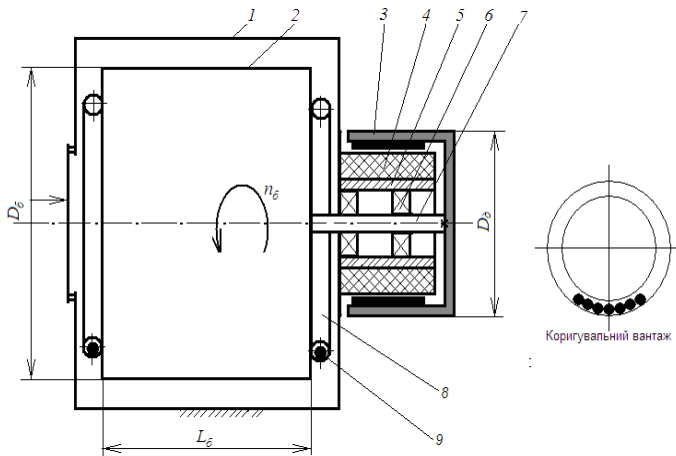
Схема приводу пральної машини з пасивним автобалансуванням барабану при віджиманні: 1- бак; 2 – барабан; 3 – ротор електродвигуна; 4 – статор електродвигуна; 5 – корпус підшипників; 6 – підшипники кочення; 7 – вал; 8 корпуси автобалансиру; 9 – коригувальний вантаж (КВ)
